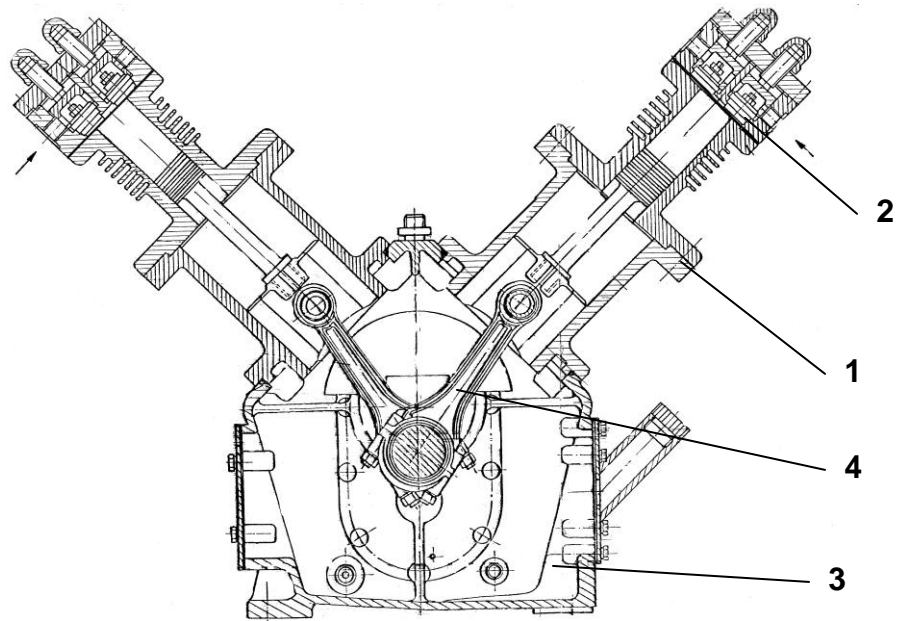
Перерезь главный компрессора V3.5.V Бустер ADP 360
